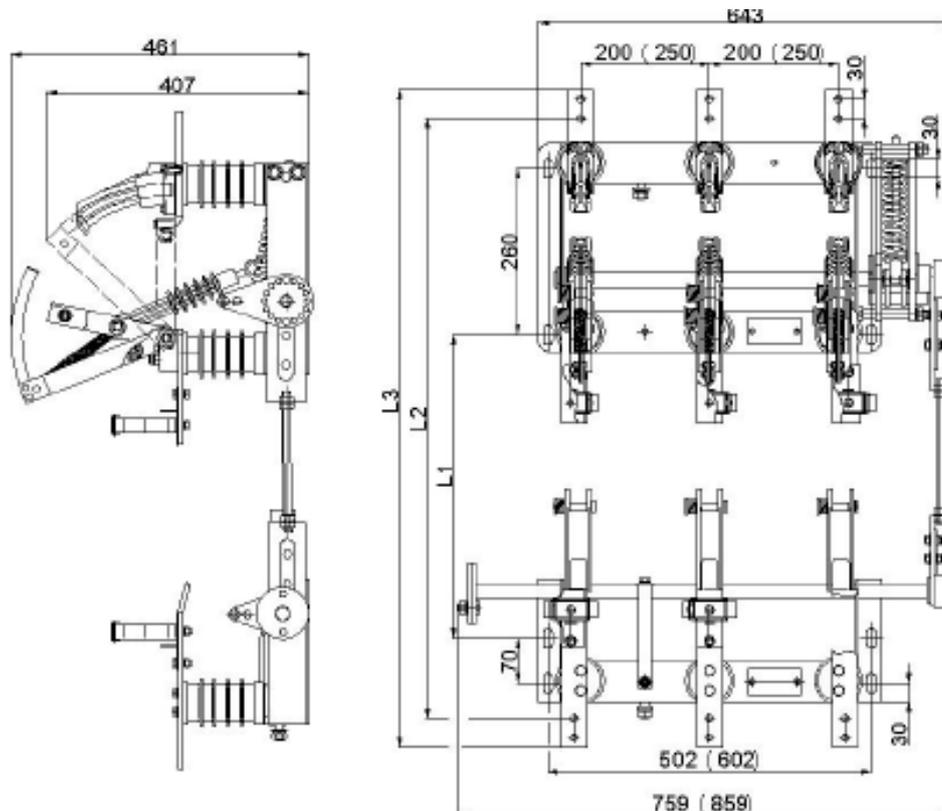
Выключатель ВНА с заземлителем и держателями под предохранитель
